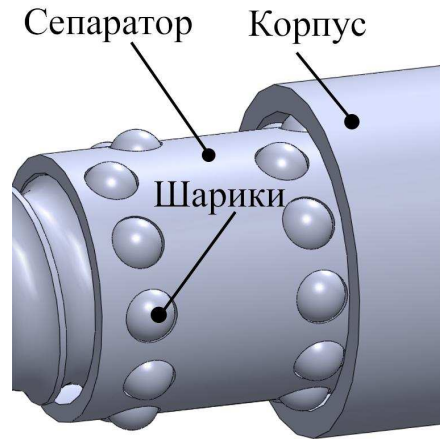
Конструкция шариковой винтовой передачи с телами качения
